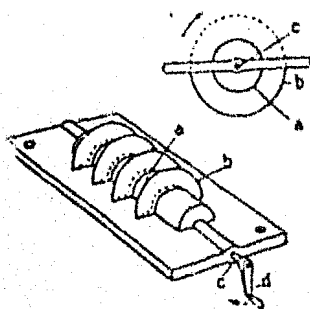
Para facilitar la extracción, las aletas, aldoando sobre placa, se montan sobre un árbol "c" y se le hace girar 180° con la manivela "d".
